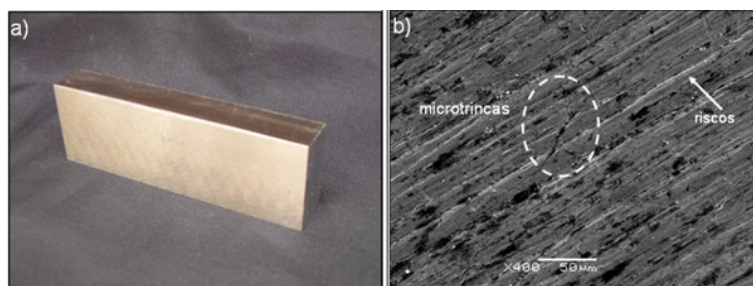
Corpo de solda soldado. (a) fotografia de um cdp com solda, (b) micrografia com microtrinca e riscos na região do ensaio de desgaste (MEV).
